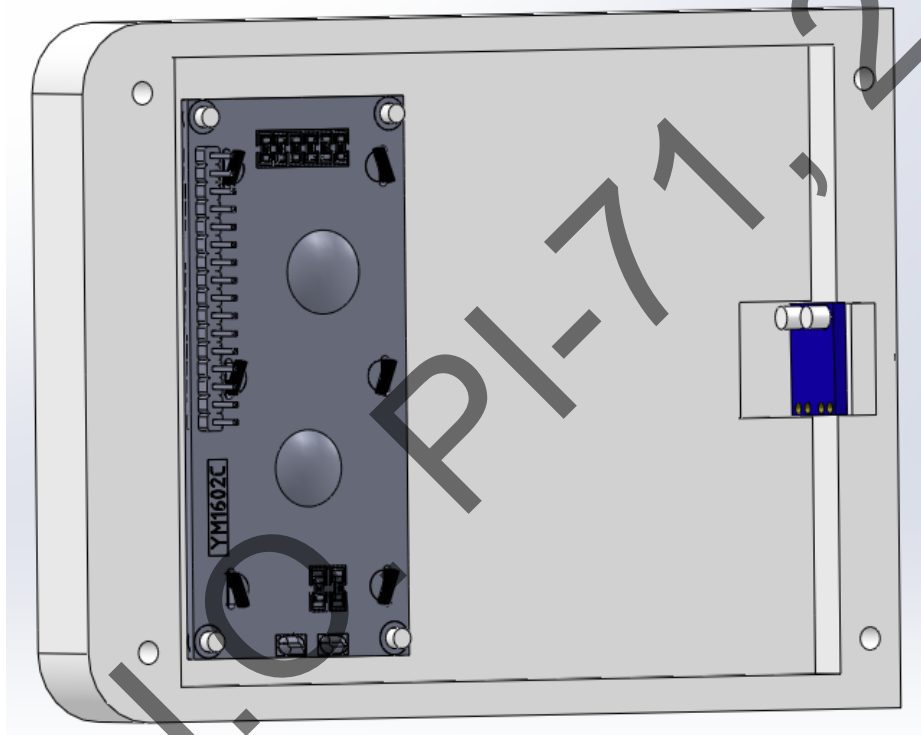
Вид знизу верхньої кришки корпусу
